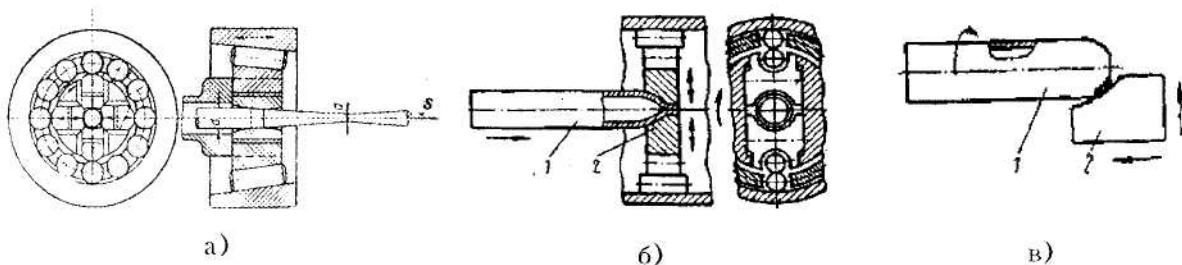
Альтернативні схеми обтиснення: 1 – заготовка; 2 – бойок;
